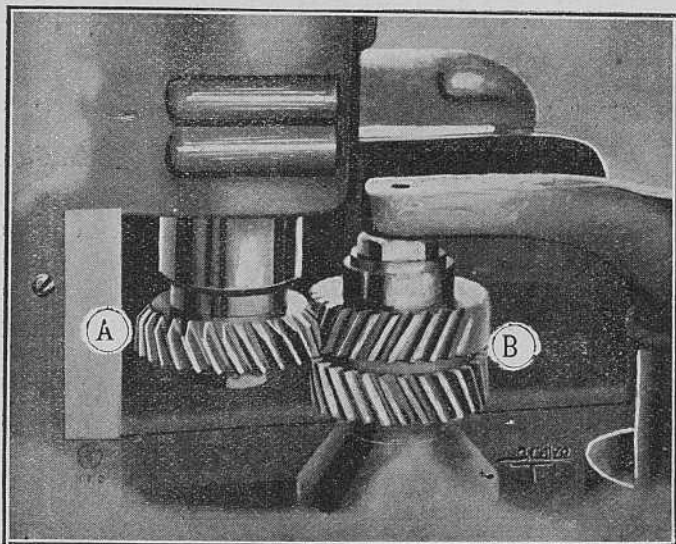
Máquina Fellow para dentar engranajes rectos y helicoidales.
